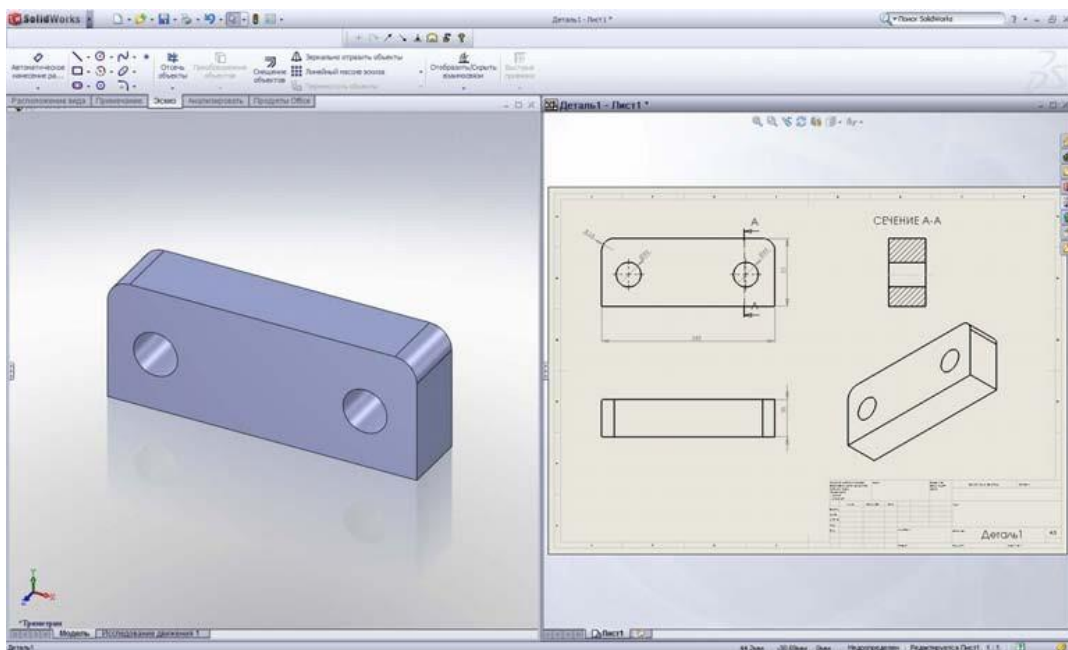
Конструкторський кресленик, асоціативно пов'язаний з геометричною моделлю
